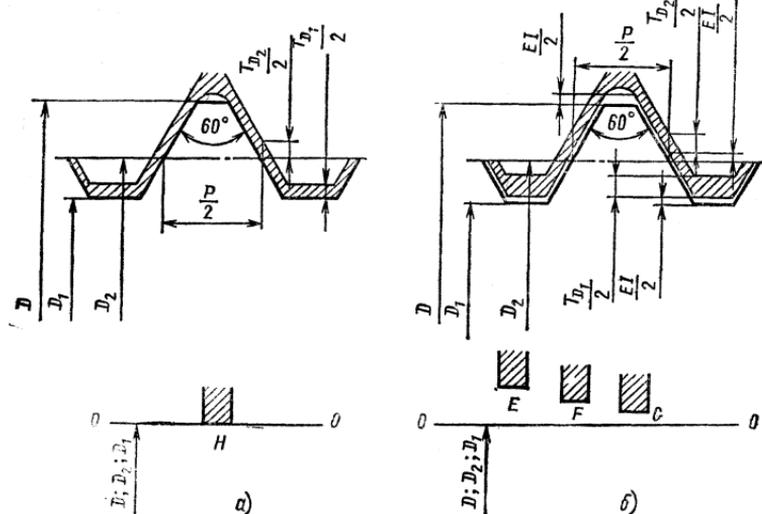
Схемы расположения полей допусков внутренней резьбы (гаек) с основными отклонениями:
